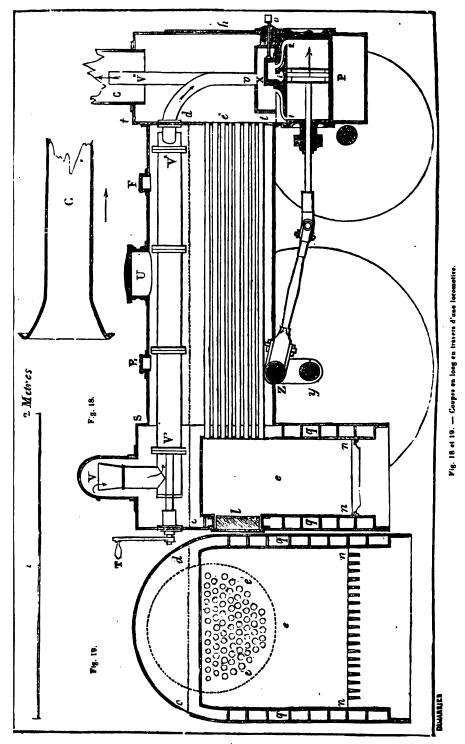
est une coupe longitudinale dans le dessin quelle on a omis beaucoup de pièces accessoires qui
